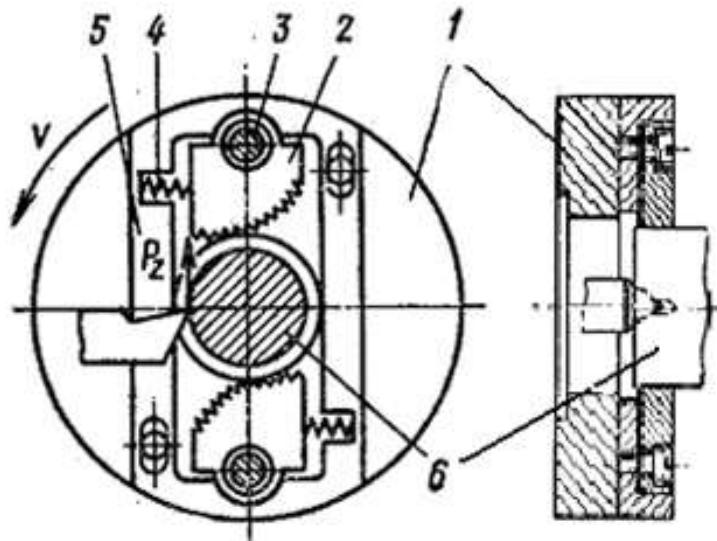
Схема токарного повідкового патрона із приводом від сил різання
